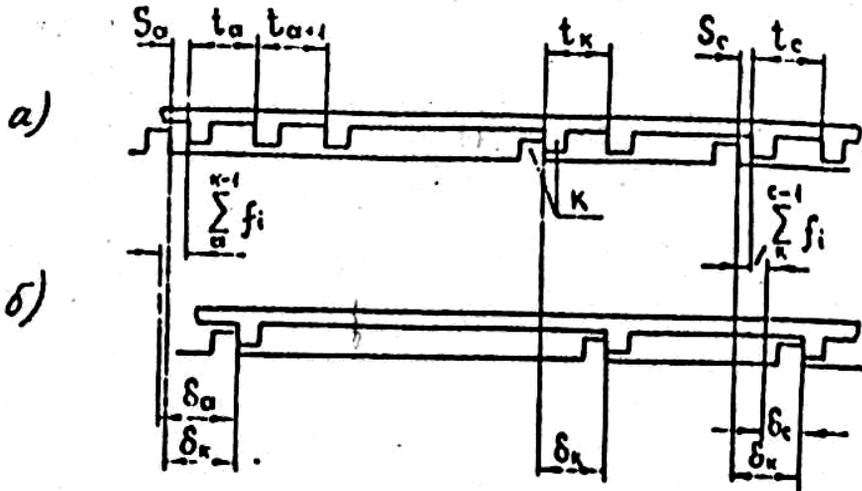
Схема перемещений витков в резьбовом соединении относительно базовой пары: а - схема ненагруженного соединения с выбранным зазором между одной парой витков винта и гайки;
